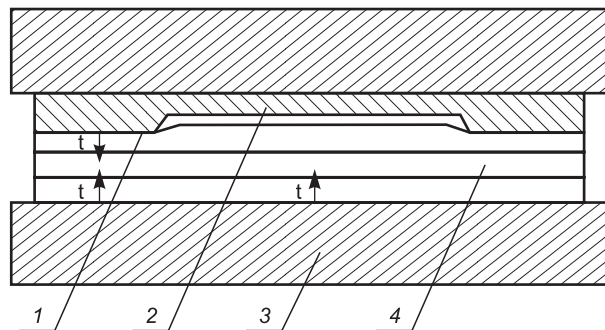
Схема устройства для изготовления рельефной фанеры: 1 – выступ пресс-формы; 2 – впадина пресс-формы; 3 – нижняя нагревательная плита; 4 – пакет шпона
